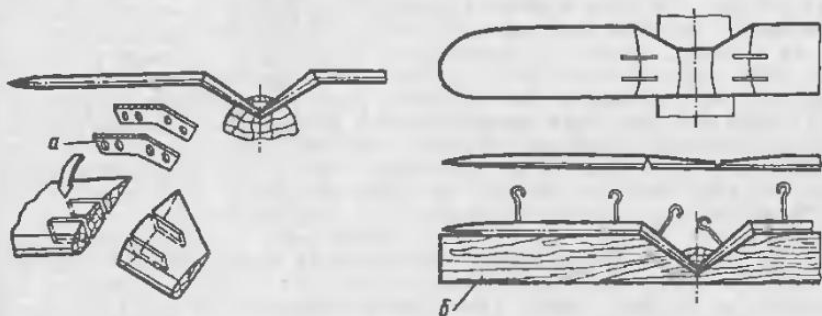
Изготовление крыла типа "чайка". Самолет И-153 "Чайка" (СССР): а - вкладыши; б - ступень
